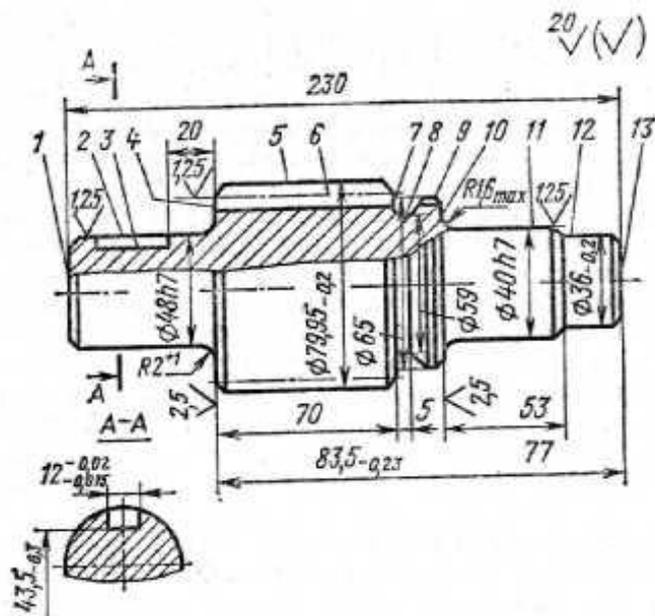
Эскиз вала-шестерни (к задаче 11.1):
